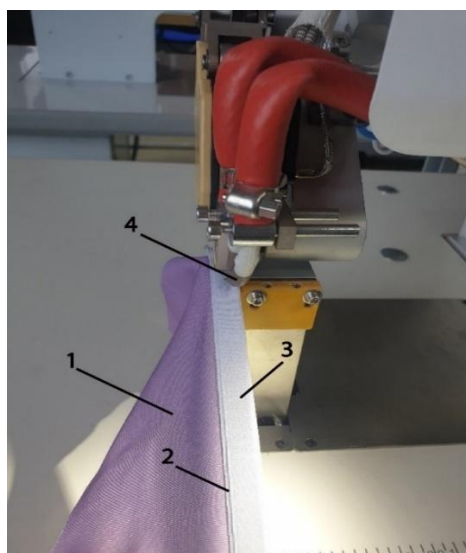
Технологический процесс образования бесшовного клеевого соединения с использованием HF – 702-02: 1 – заготовка, выкройка детали или изделие, 2 - кромка, 3 - термолента, 4 – сопла подачи горячего воздуха.
